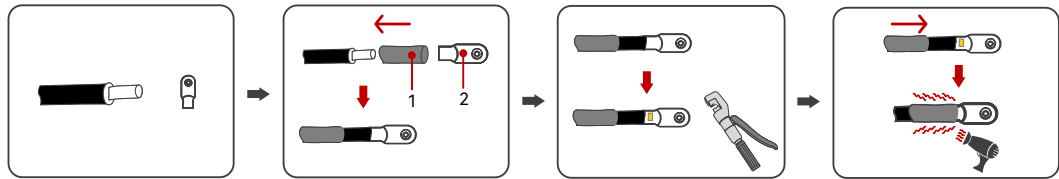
Assemblaggio dei terminali dei cavi CA
